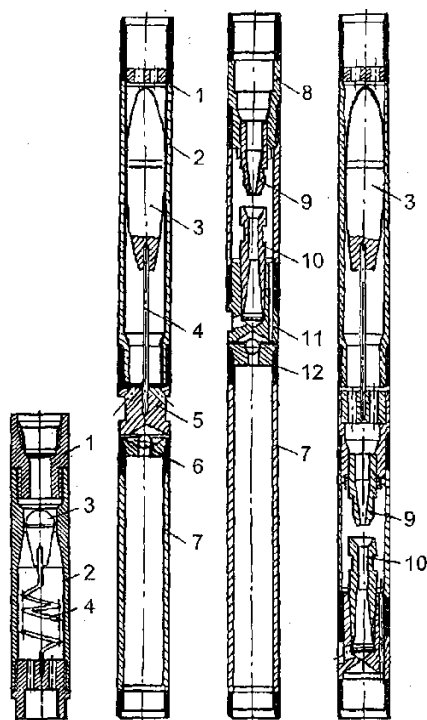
Конструктивные элементы ССК-ВИТР: а - блок вибратора; б - блок эжектора; в - комплексный блок: 1 - резьбовая втулка; 2 - корпус вибратора; 3 - боек (ударник); 4 - пружина (стержень) вибратора; 5 - переходник; 6 - шаровой клапан; 7 - присоединительный патрубок; 8 - переходник; 9 - сопло эжектора (насадка); 10 - смеситель; 11 - переходник; 12 - резиновое уплотнение
